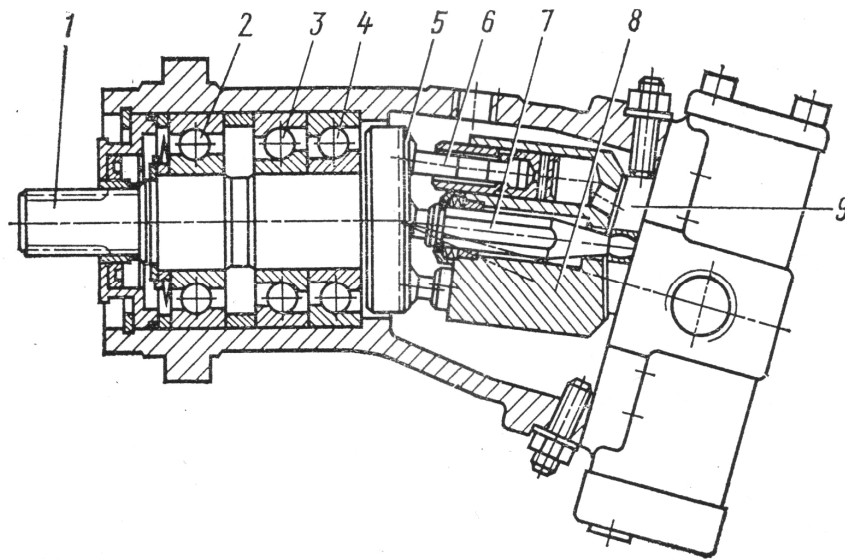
Схема аксіально-поршневого насоса: 1 – вал; 2–4 – радіальні підшипники; 5 – притискна пружина; 6 – шатун з поршнем; 7 – центральний шип; 8 – блок циліндрів; 9 – розподільник
